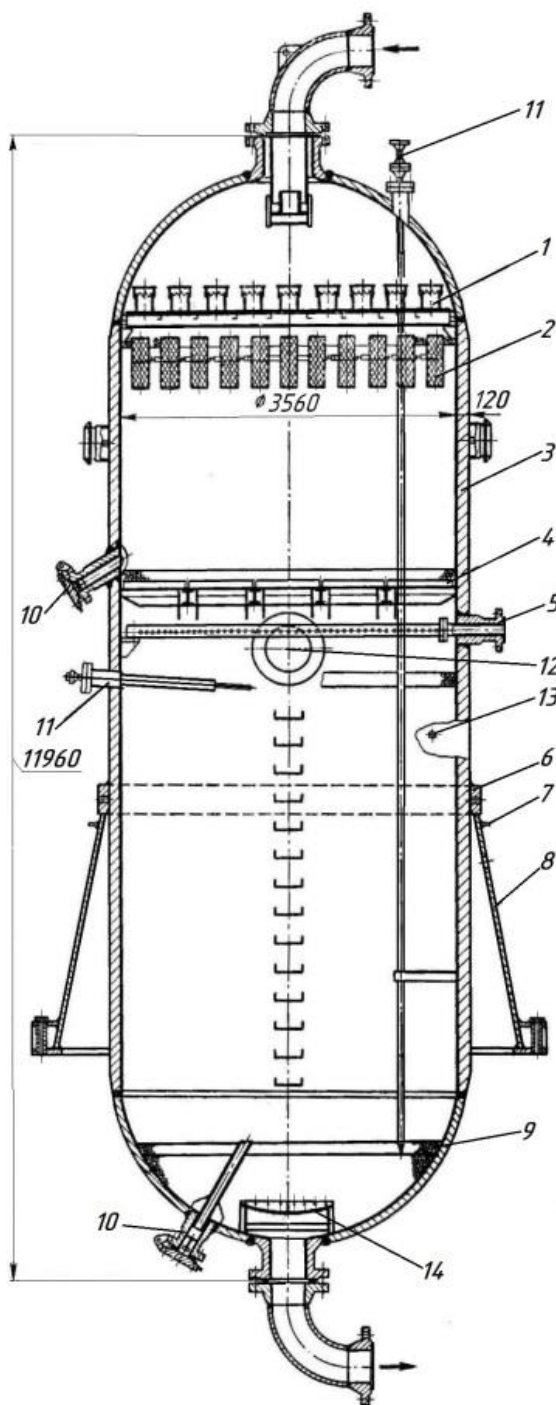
Реактор гидроочистки дизельного топлива: 1 - патрубки распределителей; 2 - фильтрующие корзины; 3 - корпус; 4 - колосниковая решетка; 5 - коллектор холодного газа; 6 - опорное кольцо; 7 - кольцо жесткости; 8 - опора коническая; 9 - слой фарфоровых шаров; 10 - штуцера выгрузки катализатора; 11 - многозонная термопара; 12 - люк; 13 - бобышки для наружных термопар, 14 – штуцер для термопары
